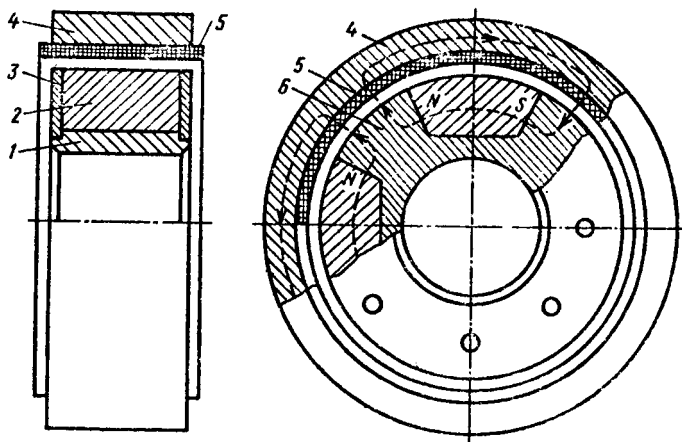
Схема конструкции электрической машины моментного вентильного двигателя
